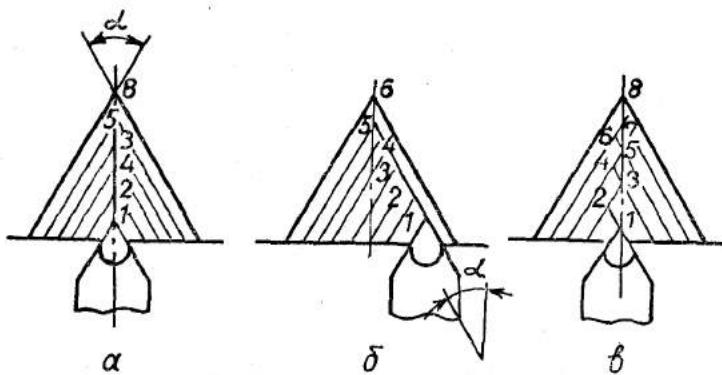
Схеми багатопрохідної обробки різцем:
